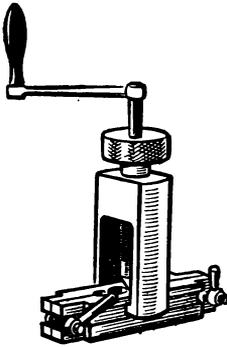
Приспособление для развальцовки трубок малого диаметра.
